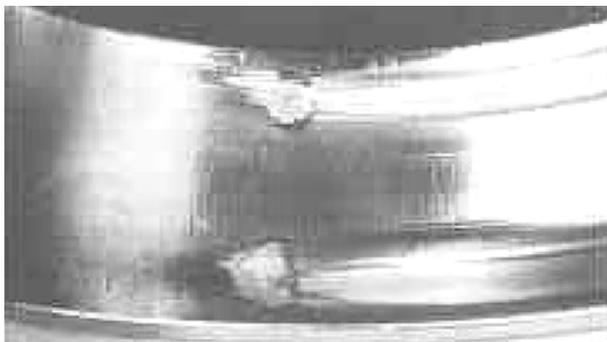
Задир на рабочей поверхности наружного кольца подшипника
